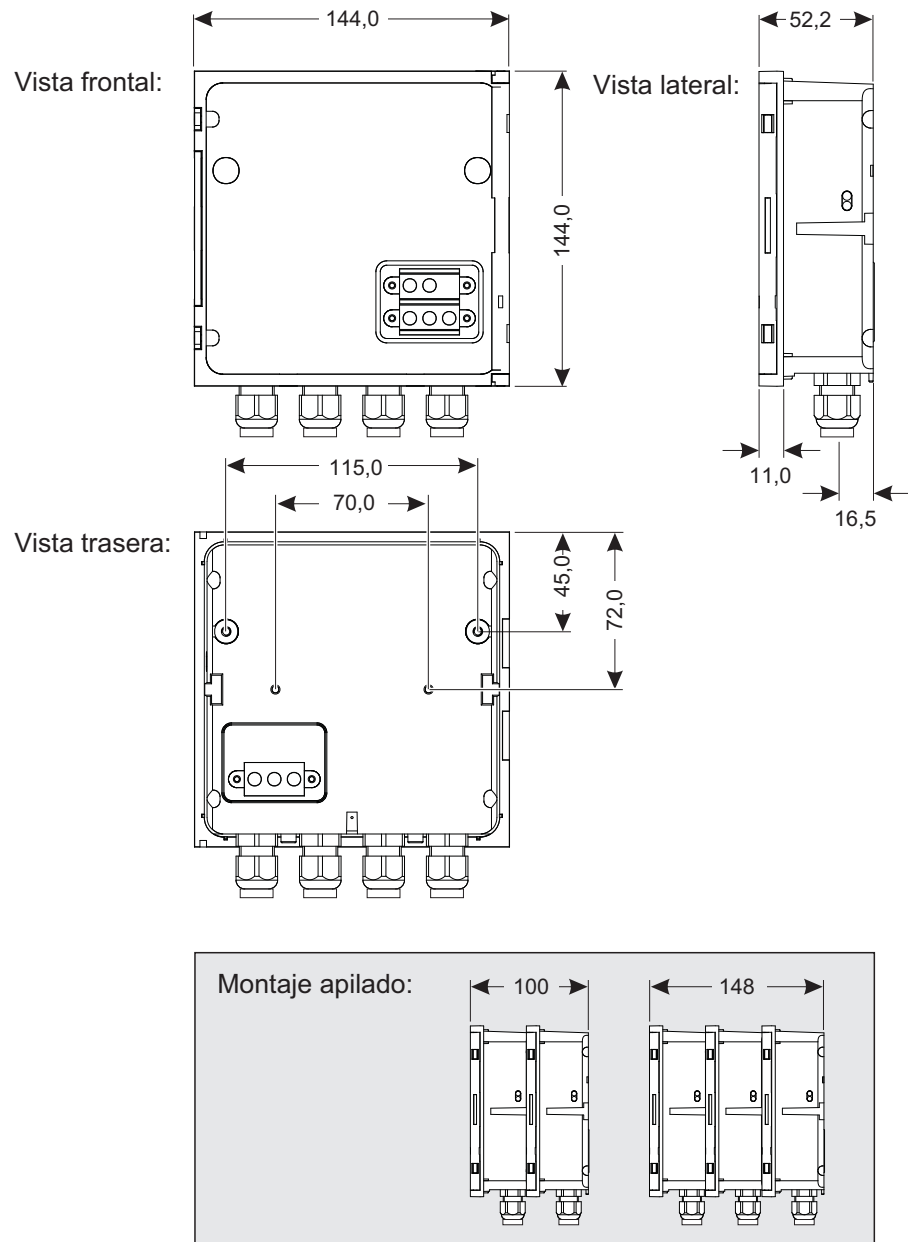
Dibujo acotado del módulo MIQ (dimensiones en mm)
